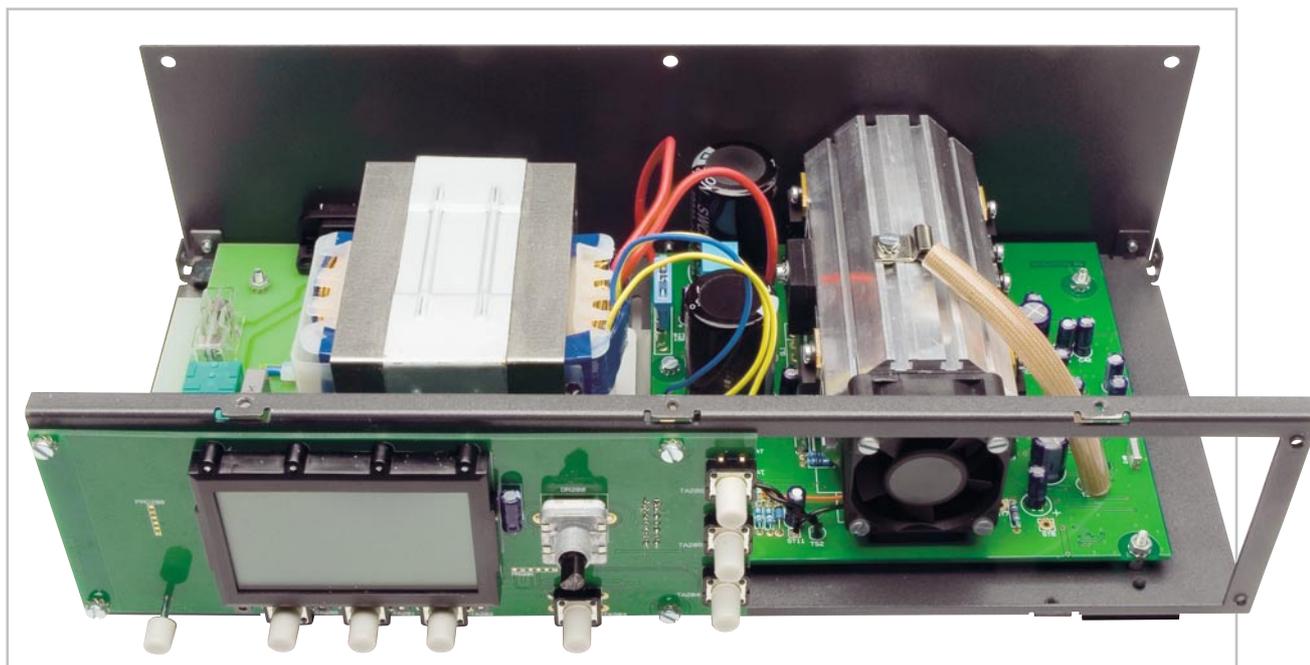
Innenansicht des fertig aufgebauten PPS 5330
